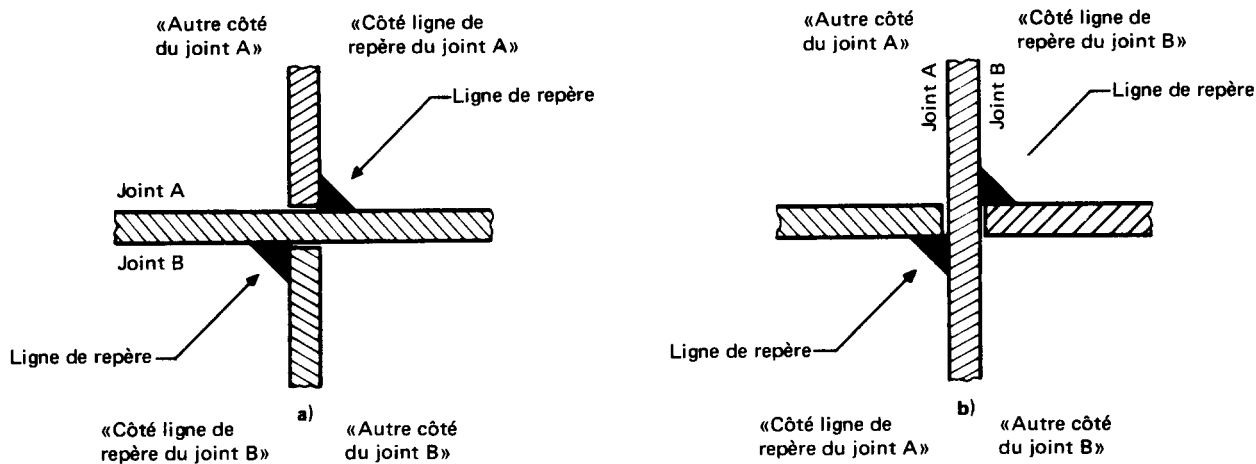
Assemblage en croix avec deux soudures d’angle
